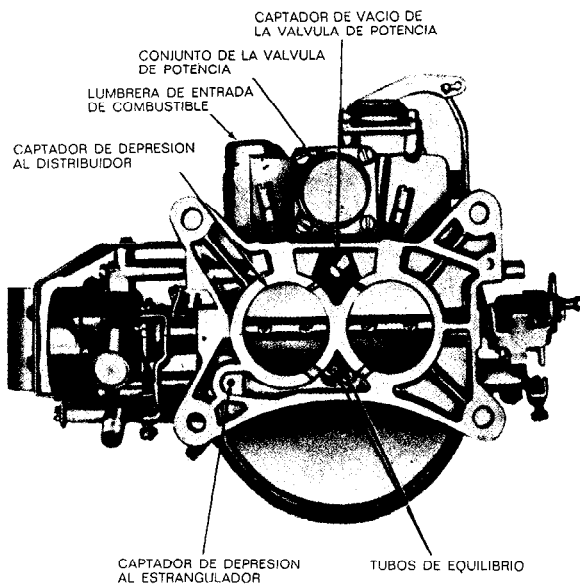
Vista desde abajo de un carburador doble (Ford Division of Ford Motor Company).
